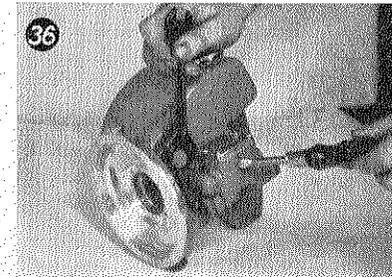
zeigt das Lösen der Befestigungsschrauben der Ölpumpe.
